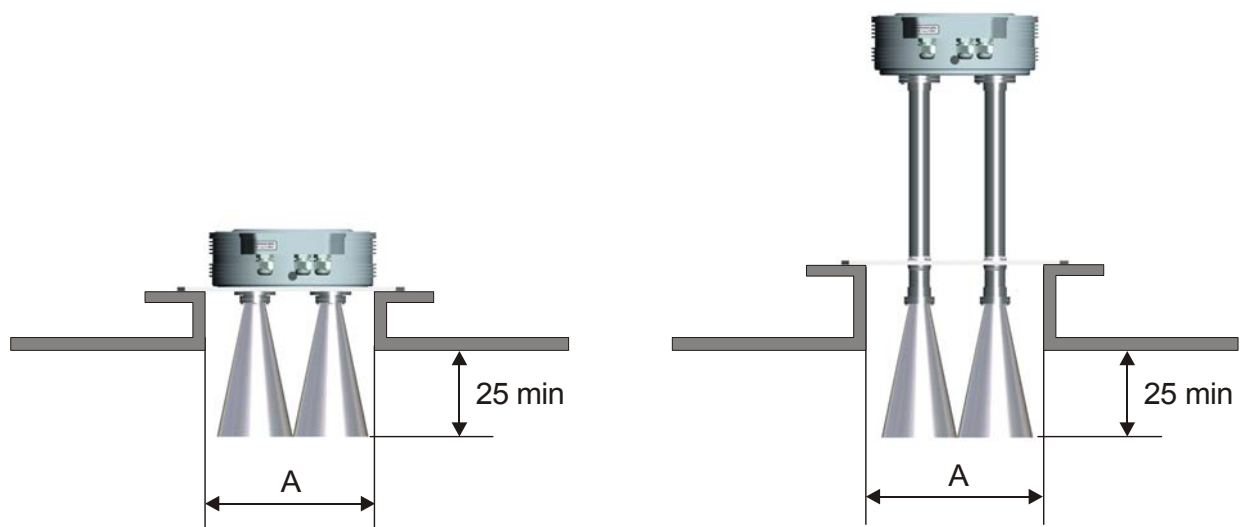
Габаритные и установочные размеры вторичного преобразователя БАРС322И
